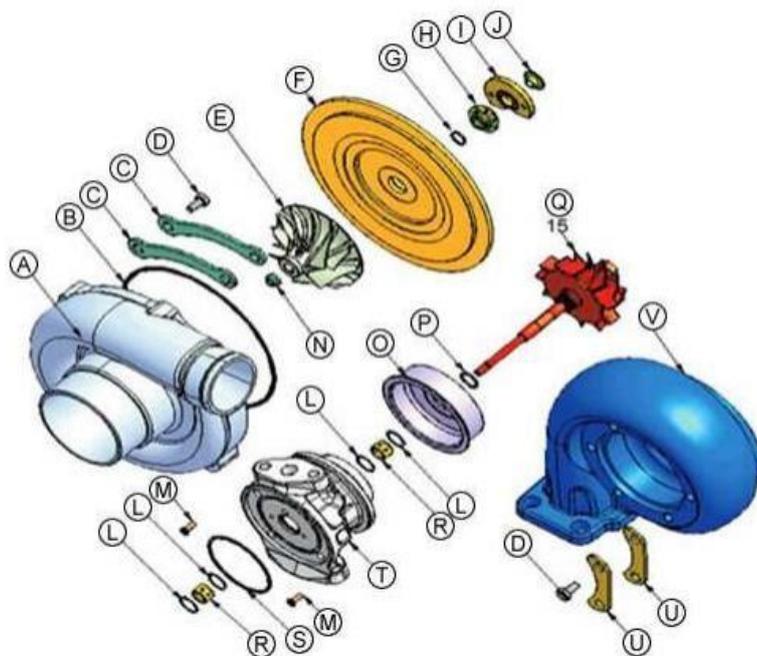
Componentes de um turbocompressor (MASTERPOWER).
